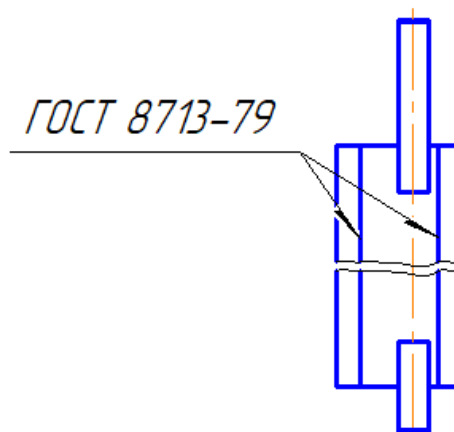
Швы, выполняемые автоматической сваркой под слоем флюса
